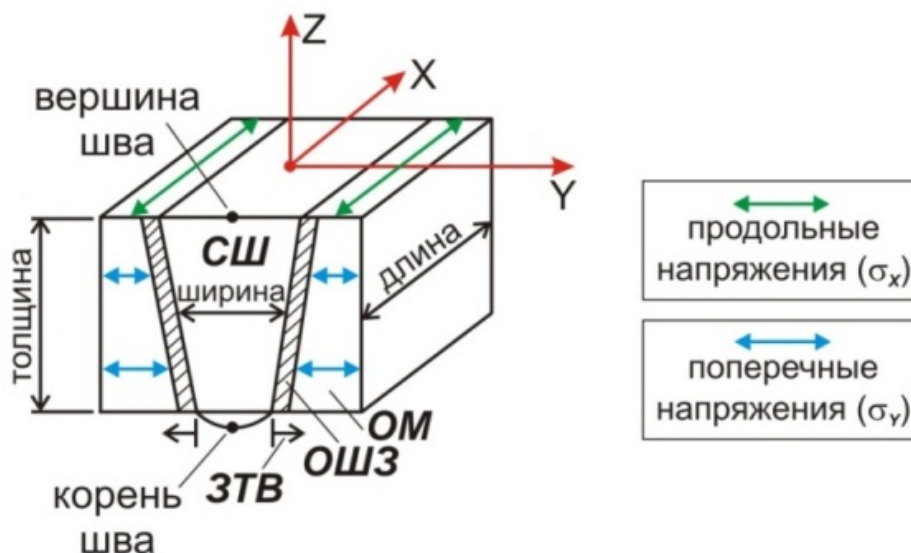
Схематическое изображение образца для исследований и действующих в нем напряжений: СШ – сварной шов, ОШЗ – околошовная зона, ЗТВ – зона термического влияния; ОМ – основной металл
